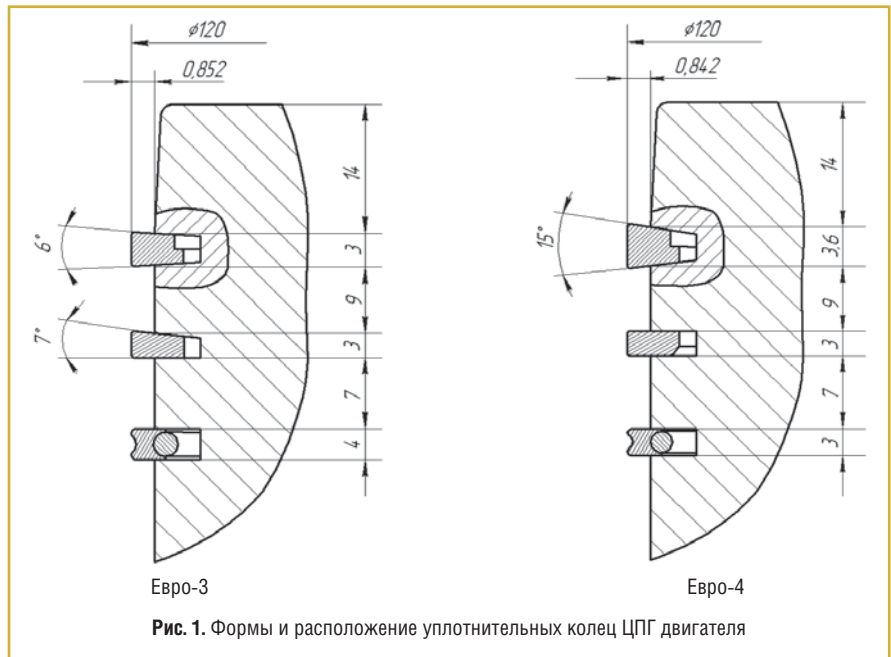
Формы и расположение уплотнительных колец ЦПГ двигателя
